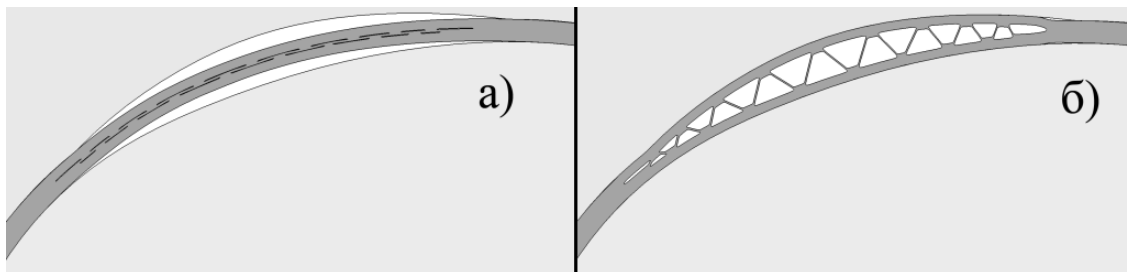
Схема процесса СПФ полой трехслойной конструкции типа лопатки, а) исходная заготовка, б) заготовка после СПФ
